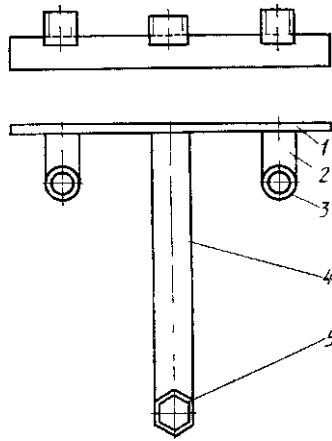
Прилад для зняття корпусу підшипника вузла активатора пральної машини: 1 - плита, 2, 4 - стійки; 3 - стакан, 5 - гніздо
